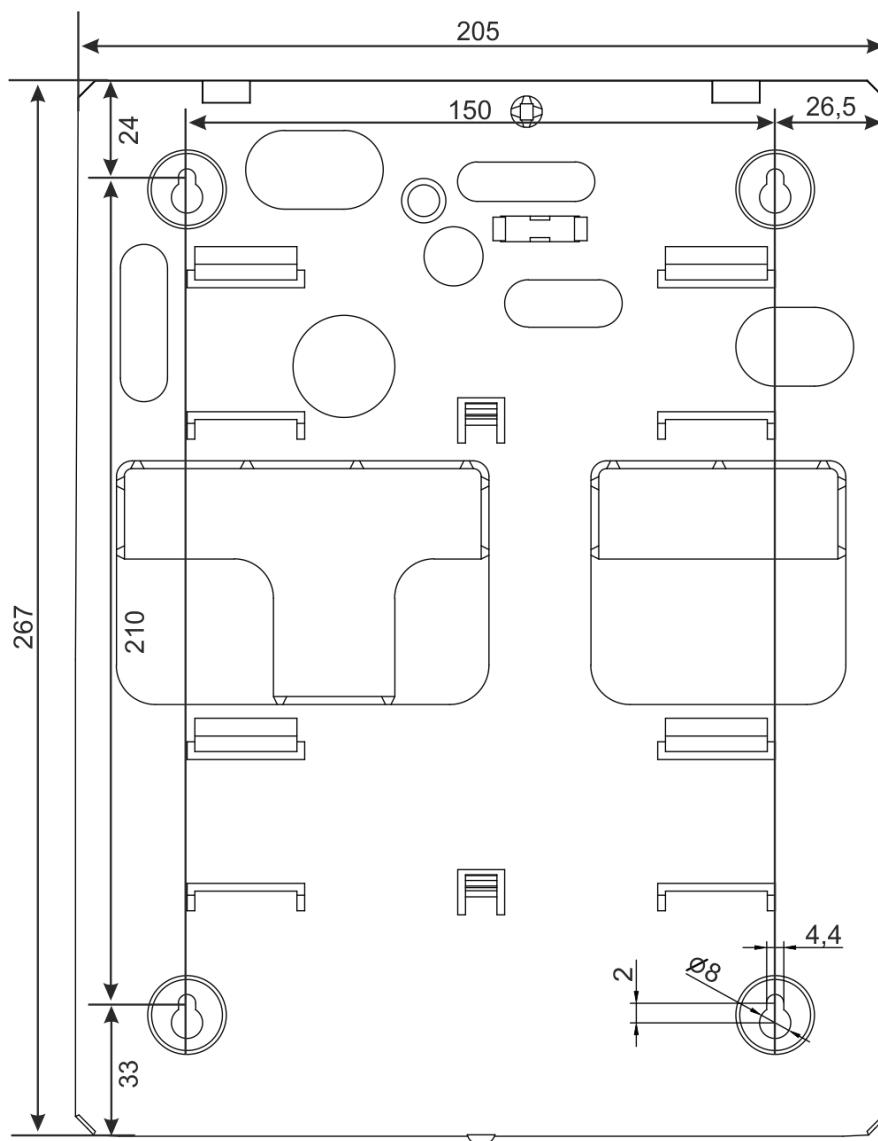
Установочный чертеж ППКПиУ серии «А24» и БА-18
